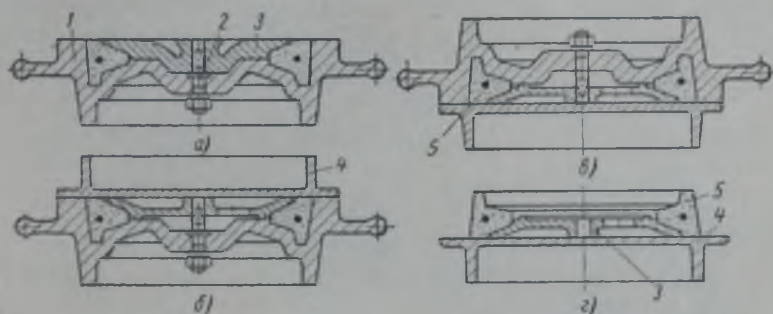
Изготовление стержня для отливки шкива насоса гидроусилителя
